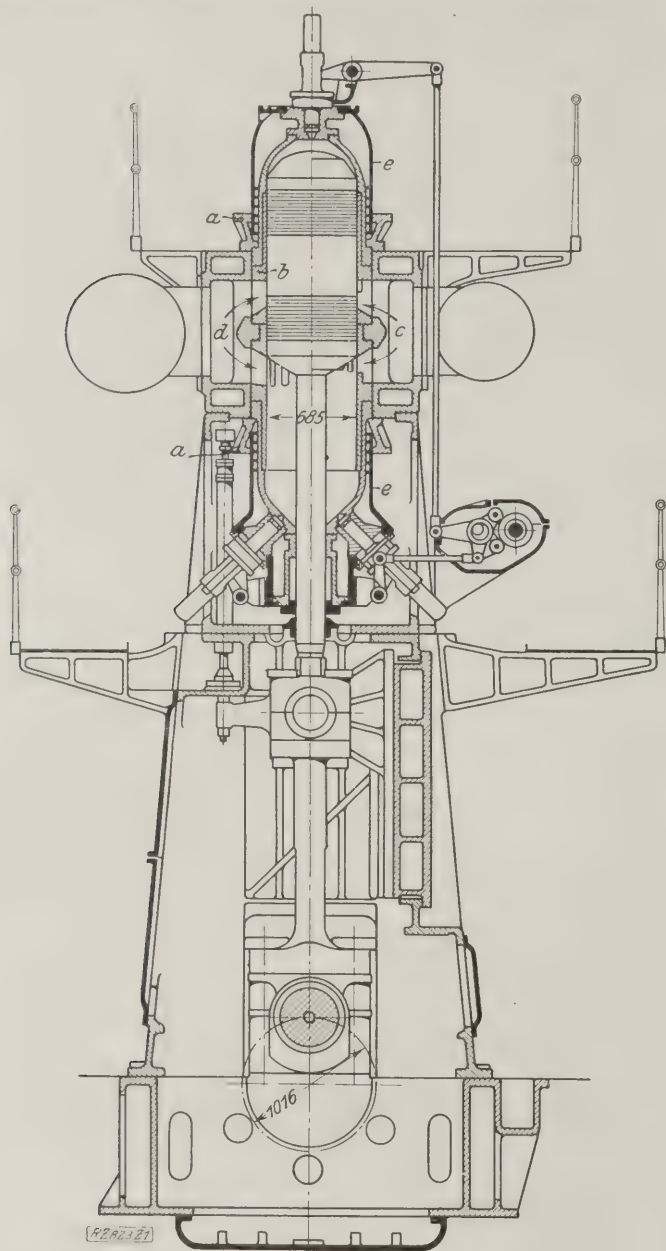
Zweitakt-Dieselmachine der Worthington Pump and Machinery Corporation.
